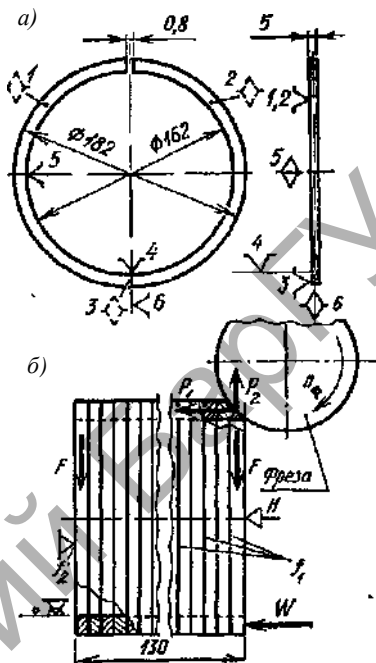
Фрезерное приспособление с гидроприводом
